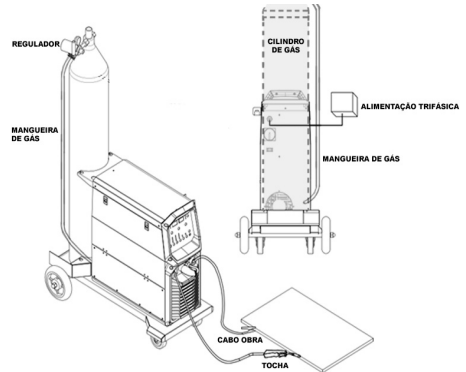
Montaje de los cables de soldadura en modo MIG/MAG con gas protector
